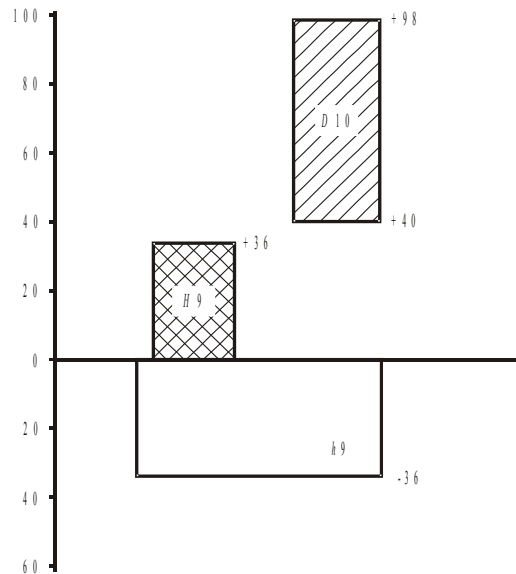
Схема расположения полей допусков сопряженных размеров пазов вала, втулки и шпонки
